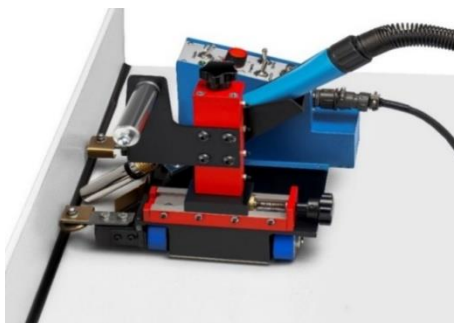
Тележка КС-5 для перемещения сварочных горелок [2]
